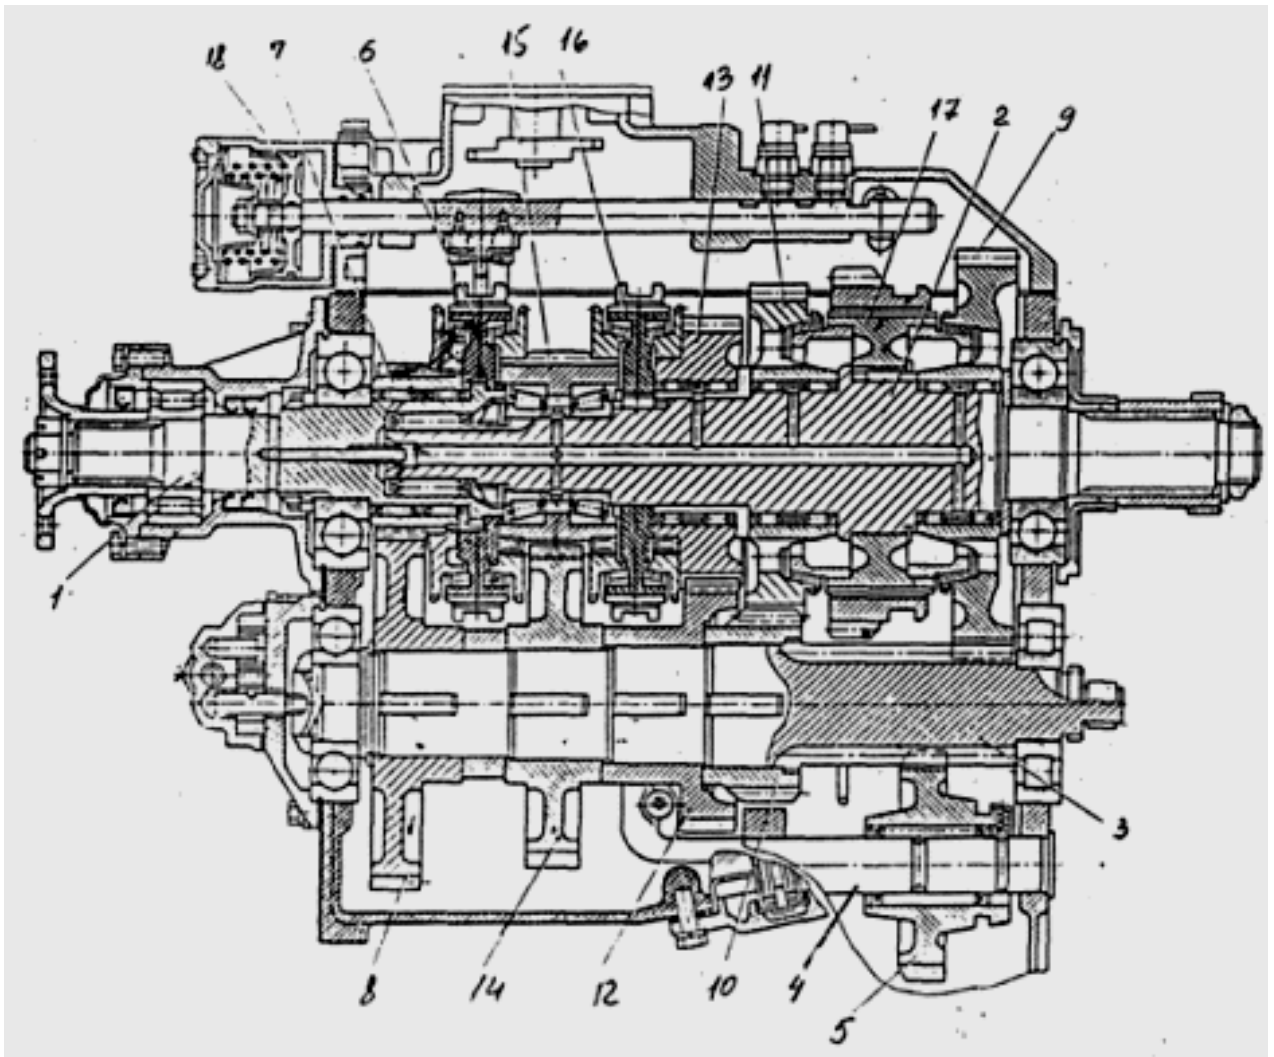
Восьмиступенчатая коробка передач (с делителем): 1 - первичный вал; 2 - вторичный вал; 3 - промежуточный вал; 4 - ось шестерни ЗХ; 5 - зубчатое колесо заднего хода; 6 - синхронизатор делителя; 7 - зубчатое колесо первичного вала; 8 - зубчатое колесо привода промежуточного вала; 9 - зубчатое колесо I и II передачи; 10 - зубчатое колесо III и IV передач промежуточного вала; 11 - зубчатое колесо II и IV передач; 12 - зубчатое колесо V и VI передач промежуточного вала; 13 - зубчатое колесо V и VI передач; 14 - зубчатое колесо VII передачи промежуточного вала; 15 - зубчатое колесо VII и VIII передач; 16, 17 – синхронизаторы
